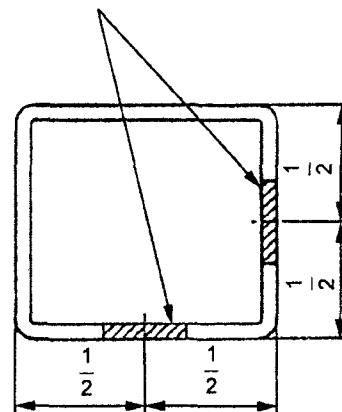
Квадратний і прямокутний поперечний переріз
